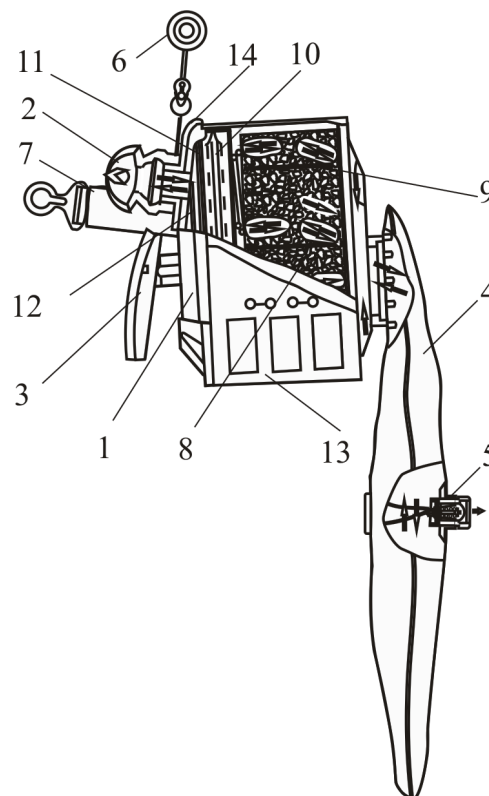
Шахтный изолирующий малогабаритный самоспасатель ШСМ-30
